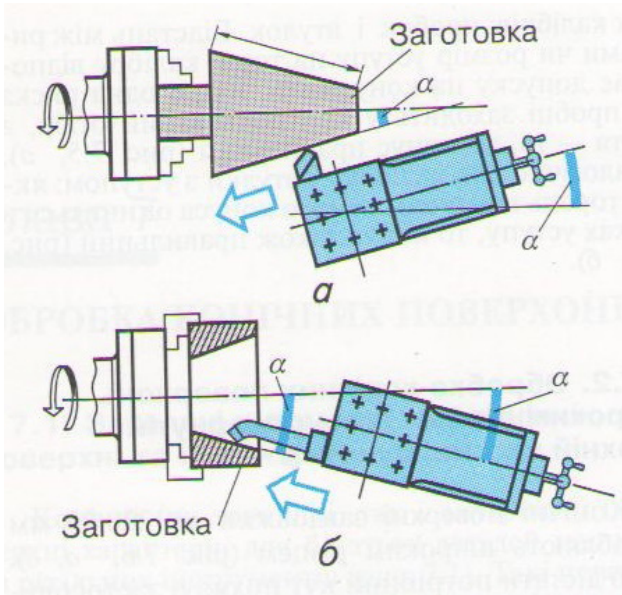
Обробка конічних поверхонь при повернутих верхніх ползках супорта:
